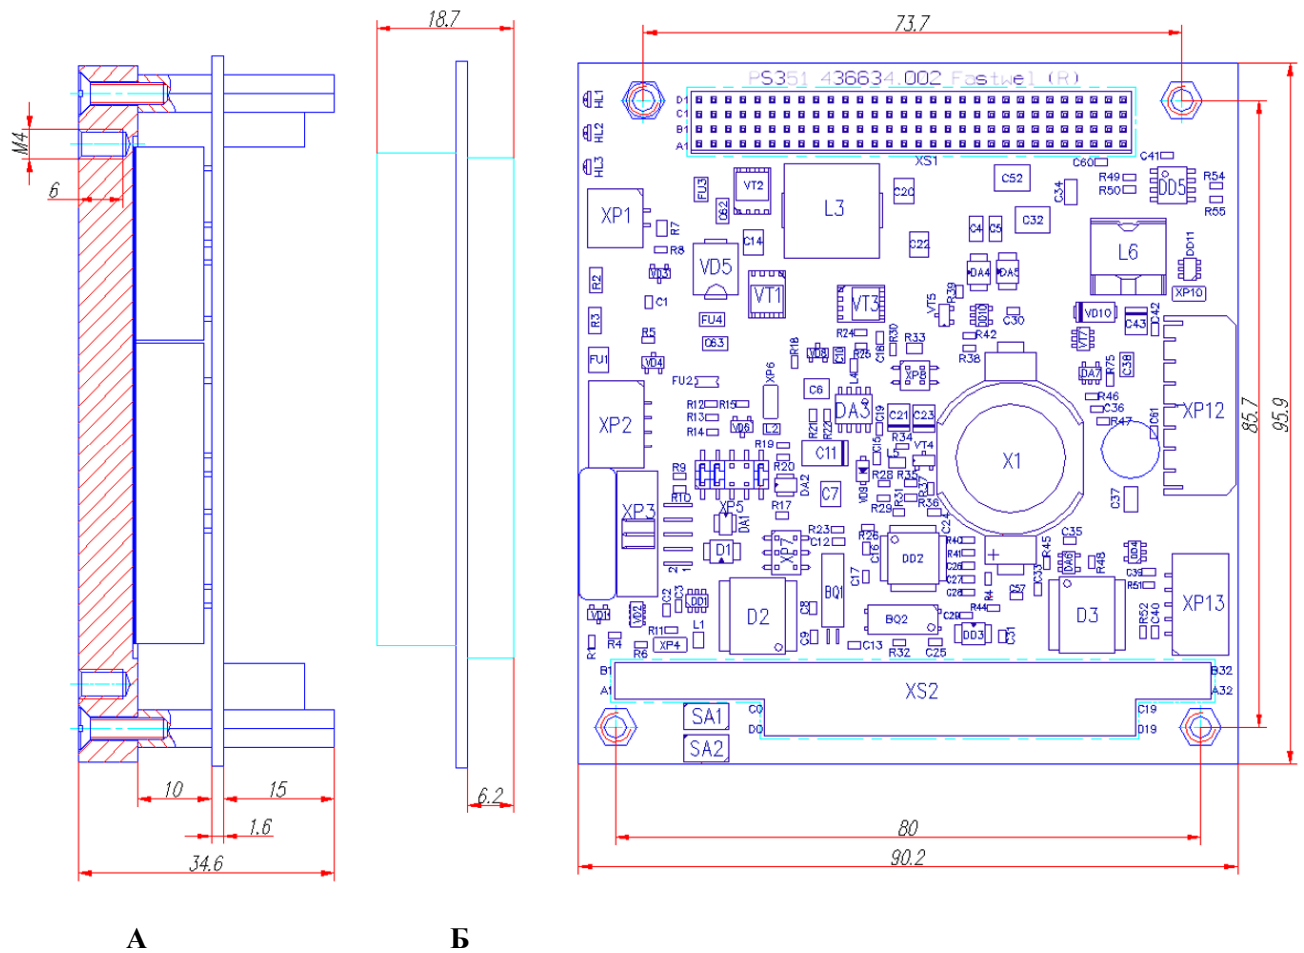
Габаритные и присоединительные размеры модуля: А – вид сбоку на исполнении PS351-01, PS351-03; Б – вид сбоку на исполнение PS351-02
